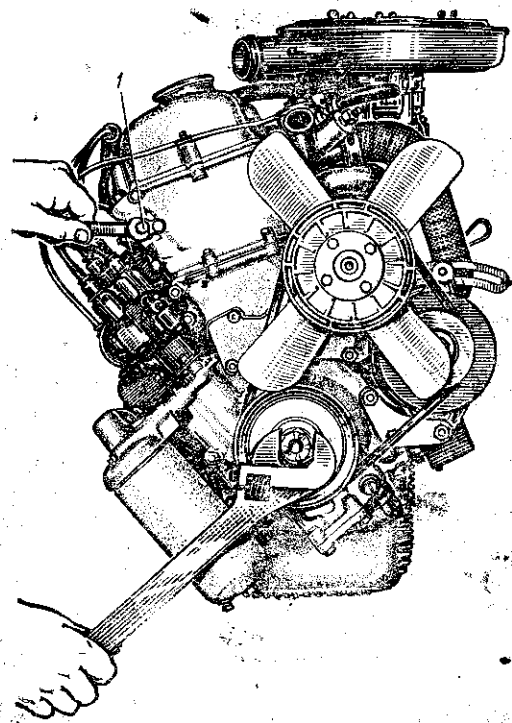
Регулировка натяжения цепи привода газораспределения:
